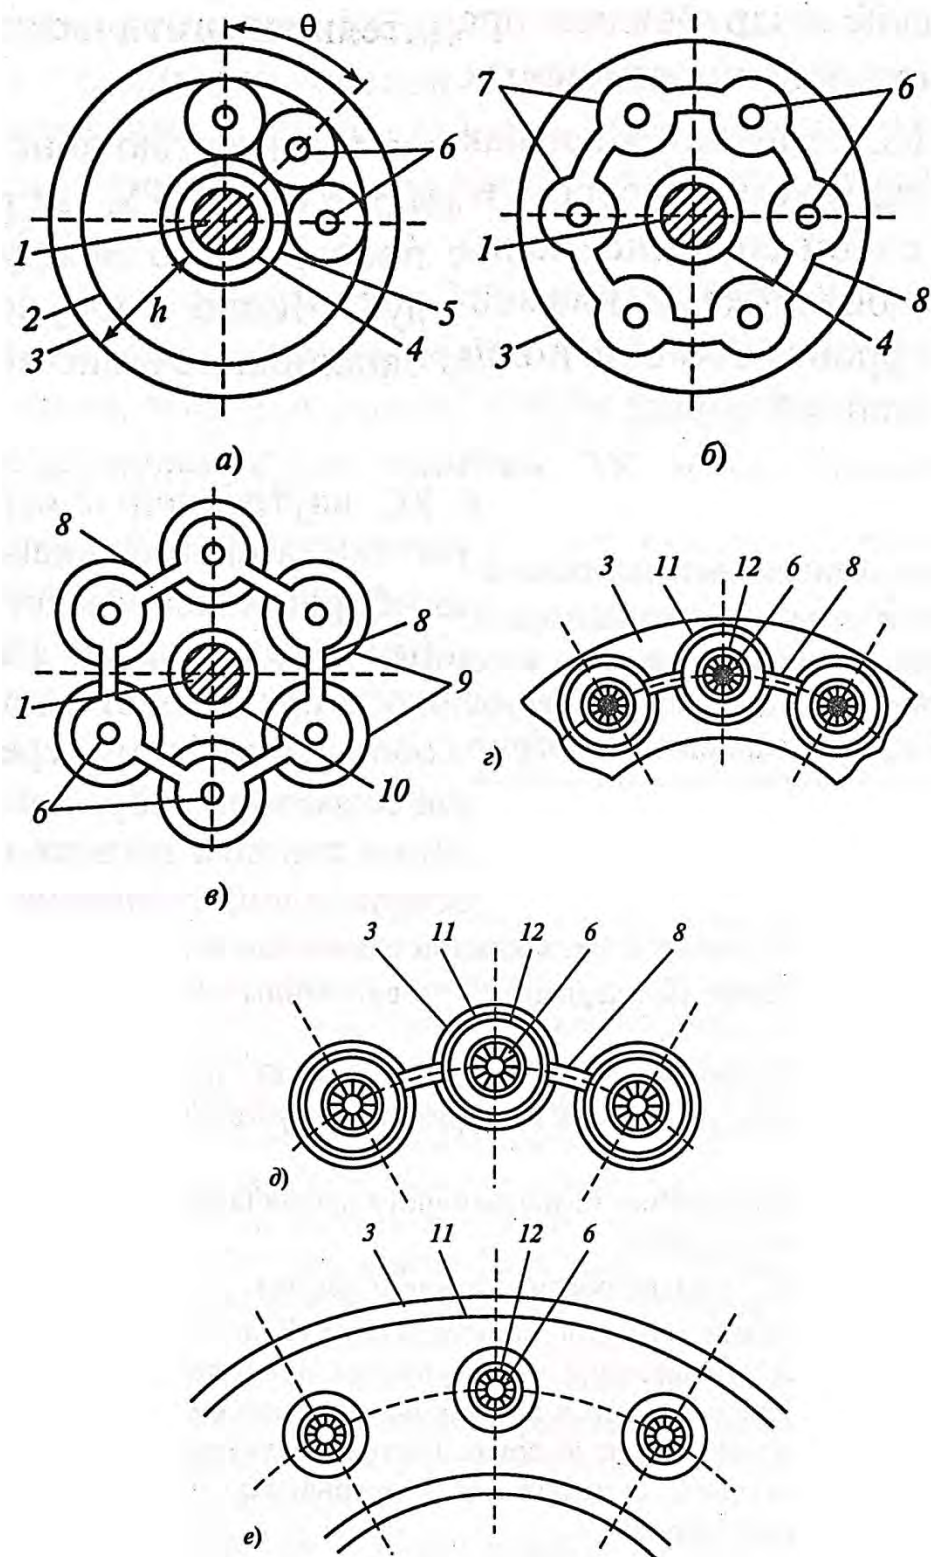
Схемы конструкций встроенных КС энергетических ГТУ (вид со стороны компрессора): а, е – кольцевые, б, д – трубчато-кольцевые; в, г – секционные; 1 – вал ротора ГТУ; 2 – наружная обечайка кольцевой пламенной трубы; 3 – наружный (кольцевой) корпус камеры сгорания; 4 – внутренний корпус, 5 – внутренняя обечайка кольцевой пламенной трубы, 6 – форсунки; 7 – отдельные пламенные трубы; 8 – патрубок для переброски пламени; 9 – корпус; 10 – кожух вала, 11 – пламенная труба, 12 – завихритель.
